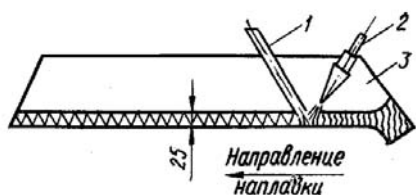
Схема наплавки лезвия лемеха твердым сплавом с помощью газовой горелки: 1 — пруток твердого металла; 2 — горелка; 3 — лемех
